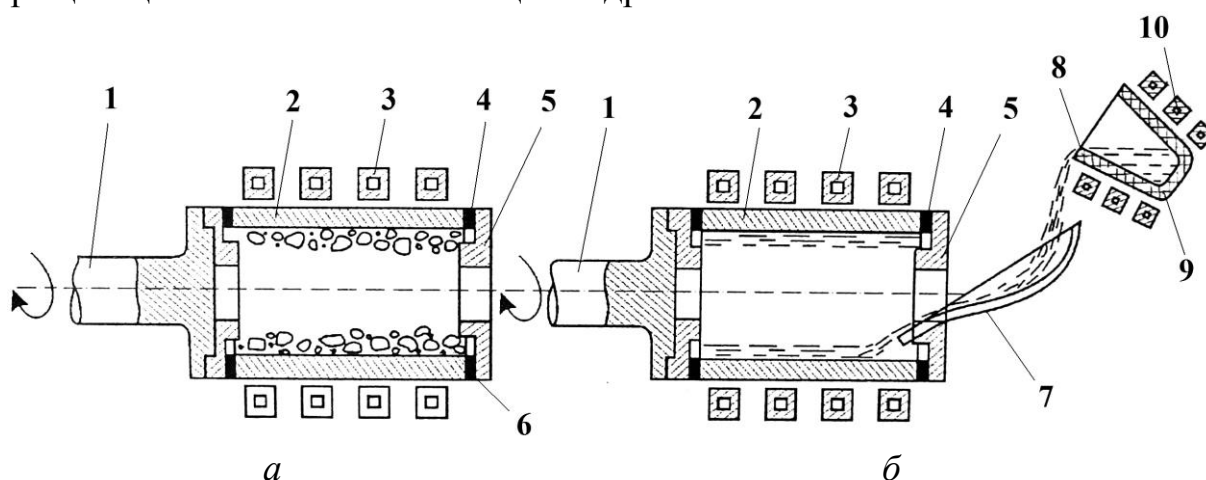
Принципиальные схемы индукционной центробежной наплавки с использованием твердого (а) и расплавленного (б) присадочного материала:
